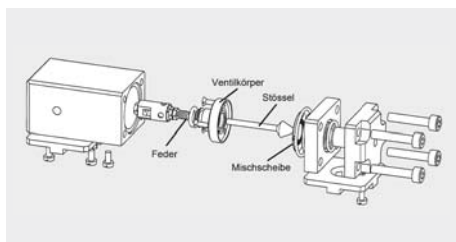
Explosionszeichnung des Ventilmischers von Ehrfeld BTS.
